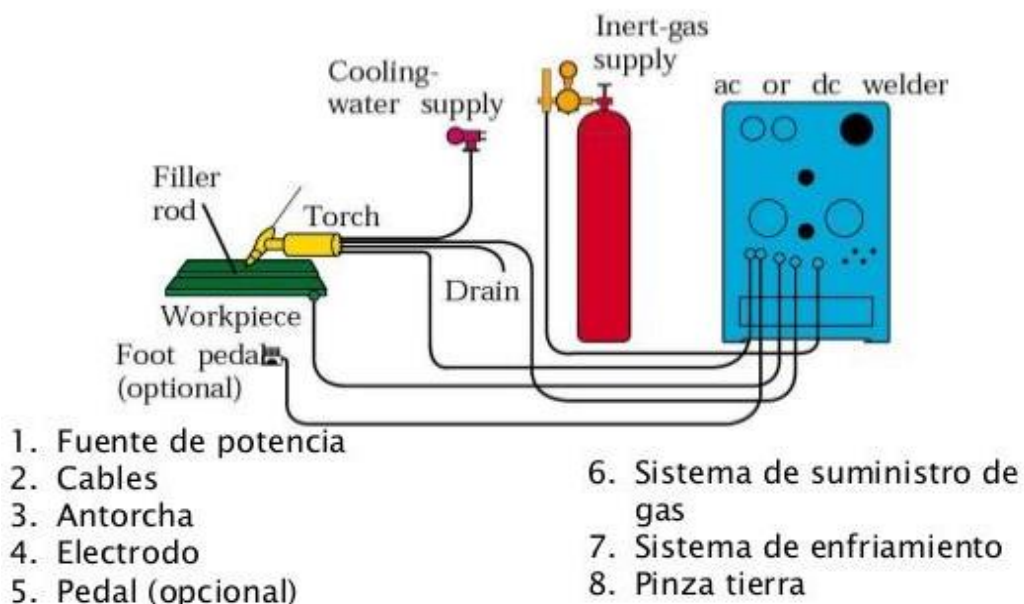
Diagrama de conexión para un sistema de soldadura GTAW.
